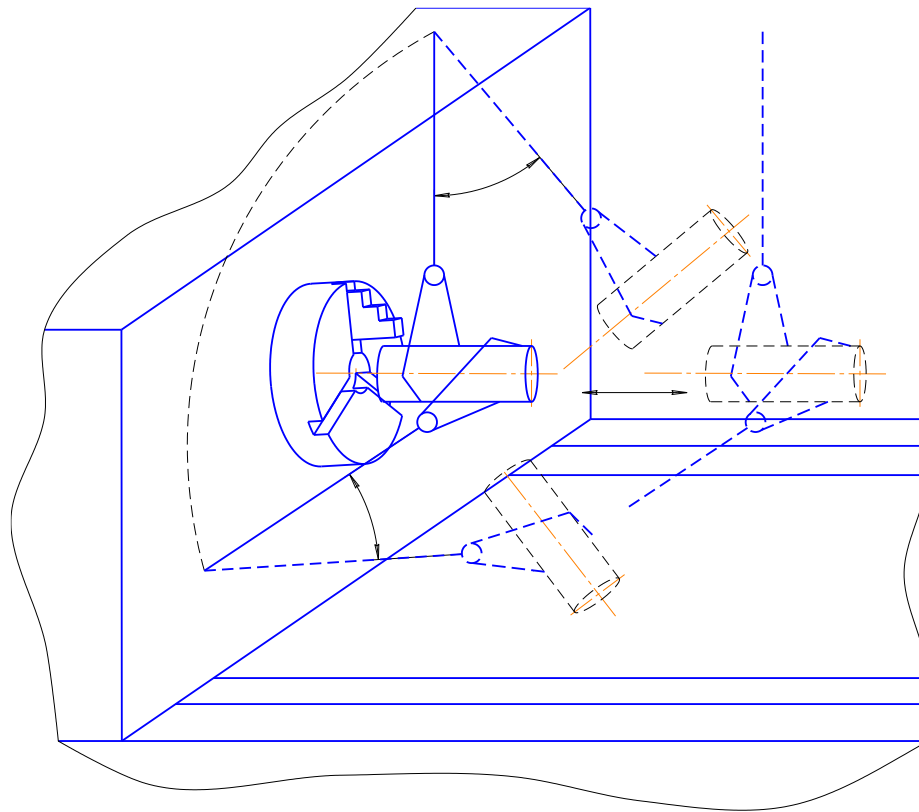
Варіанти переміщення заготовок на робочу позицію верстата:
